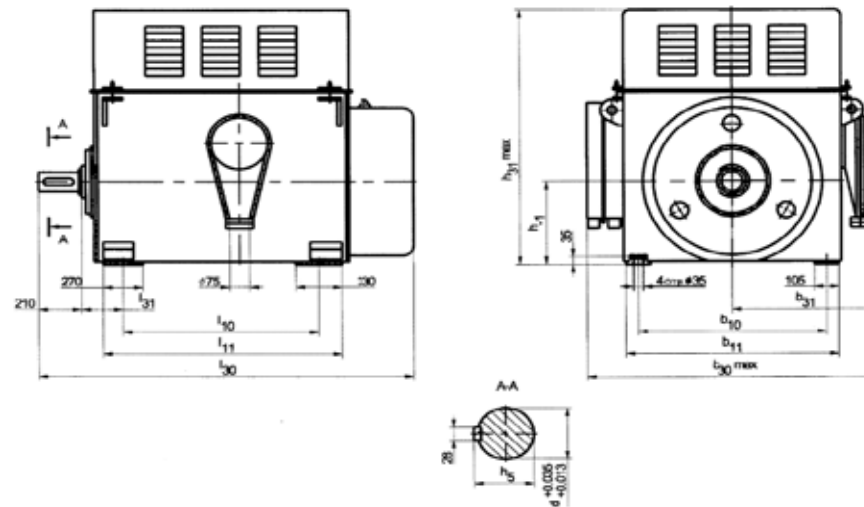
габаритный чертеж электродвигателя АК4-400ХК-4УЗ
